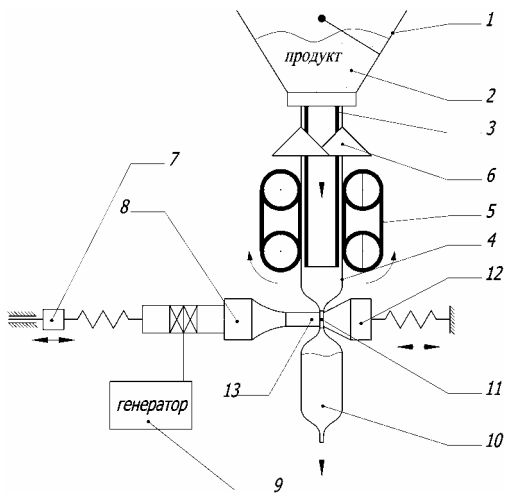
Схема формирования поперечного герметизирующего шва ультразвуковой сваркой
